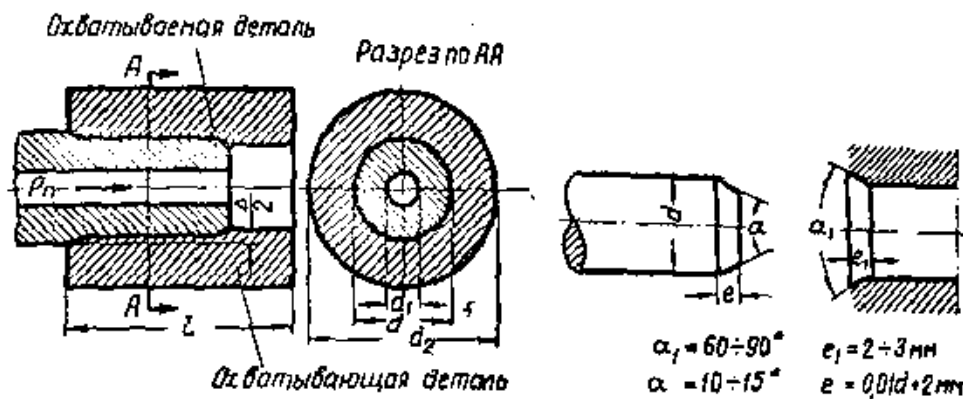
Схема соединения в процессе запрессовки, форма и размеры фасок деталей, собираемых под прессом.
